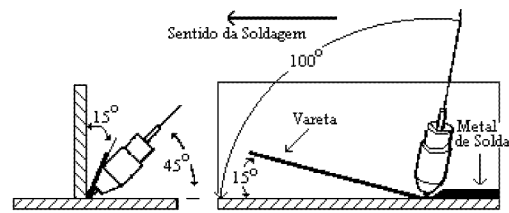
Soldagem TIG de Filete na Posição Horizontal.
